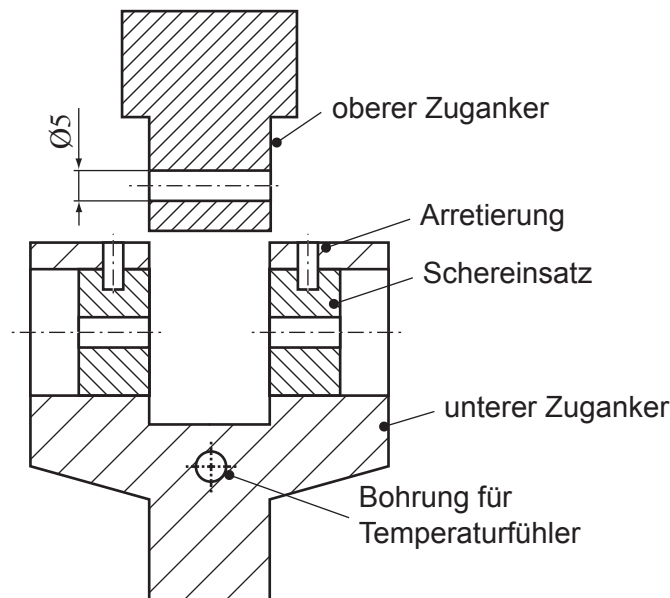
Schervorrichtung für die Universalprüfmaschine
